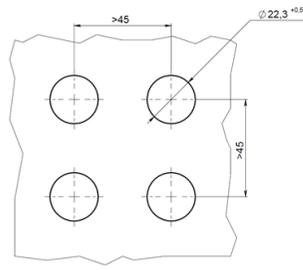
Размеры установочных отверстий для грибовидных выключателей
